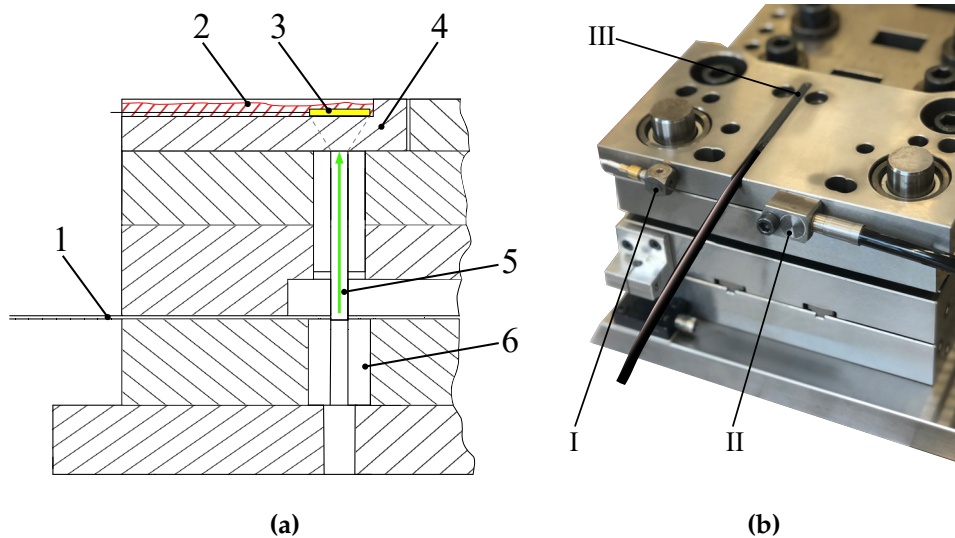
Sensoren am Schneidwerkzeug, die in dieser Arbeit verwendet werden; (a) Schneidwerkzeug in der Schnittdarstellung; Bandmaterial (1), Kleber (2, rot), Piezosensor (3, gelb), Stempelhalteplattensegment (4), Schneidstempel (5), Schneidplatte (6), Kraftfluss (grün), (b) Schneidwerkzeug mit einem Stempelhalteplattensegment und angebrachten Sensoren; Beschleunigungssensor (I), Körperschallsensor (II), Piezosensor (III)
